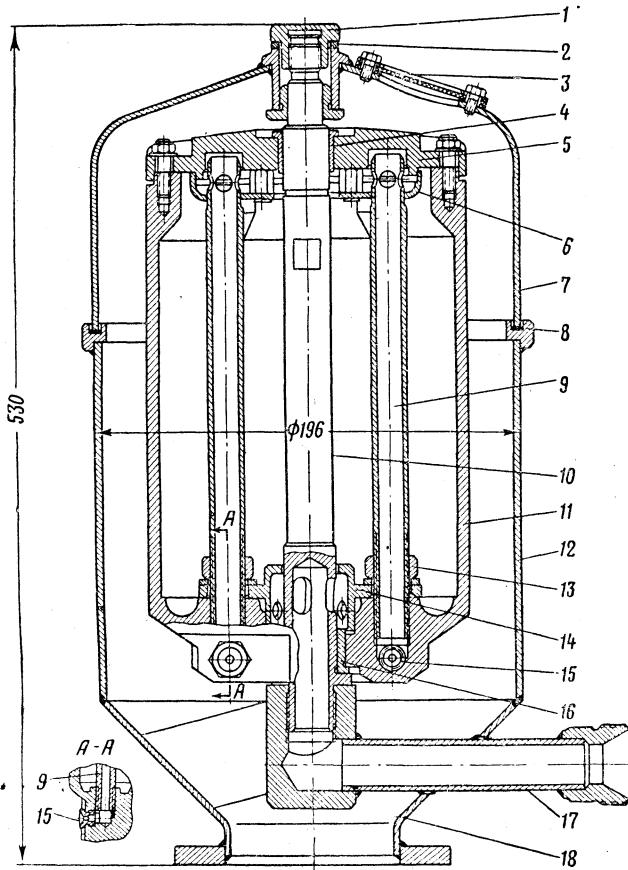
Центробежный масляный фильтр дизеля 2Д100:
